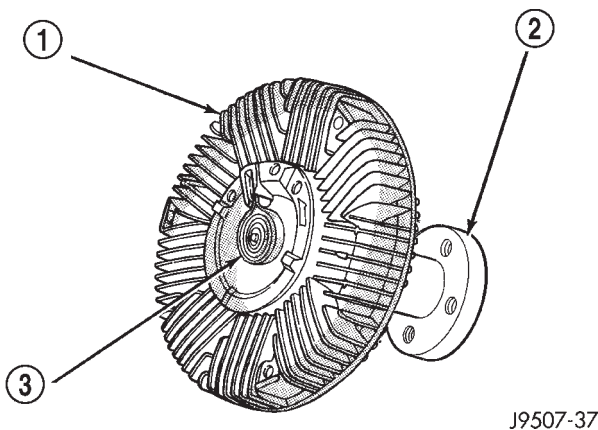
Transmisión viscosa del ventilador - Motor 2.5L
